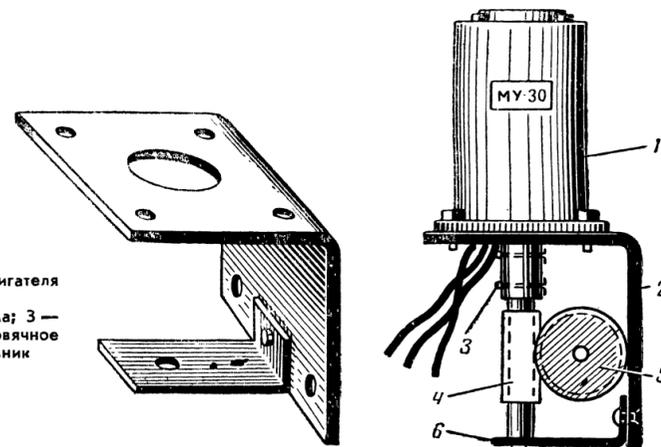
Установка тягового двигателя и редуктора: 1 — электродвигатель; 2 — рама; 3 — втулка; 4 — червяк; 5 — червячное колесо; 6 — опорный угольник
